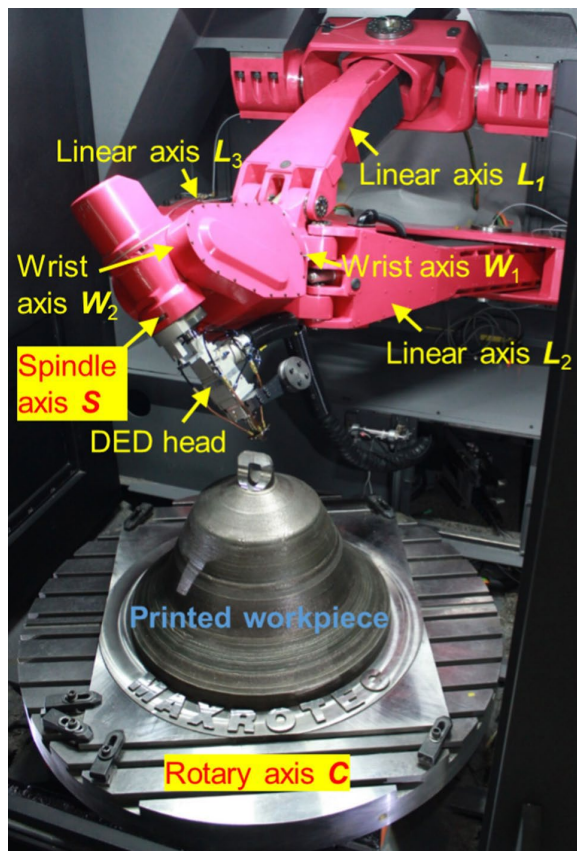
Шестиподвижная система относительного манипулирования с пятиподвижным и одноподвижным модулями в устройстве для 3D печати металлических изделий
